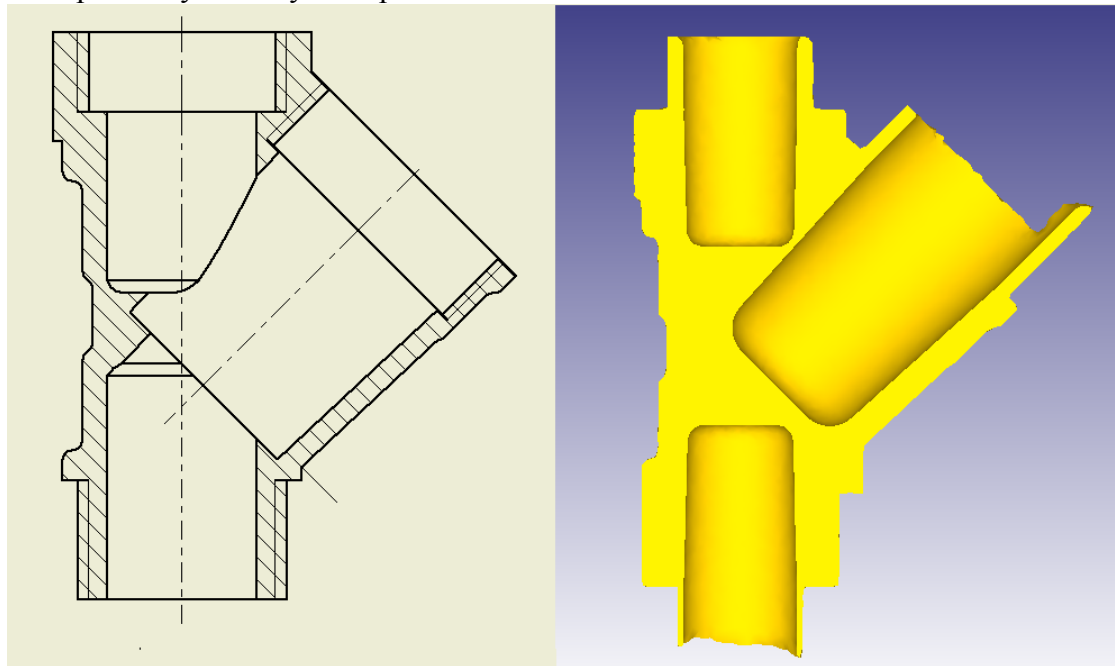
Чертеж детали "Корпус фильтра" и Заготовка после штамповки
